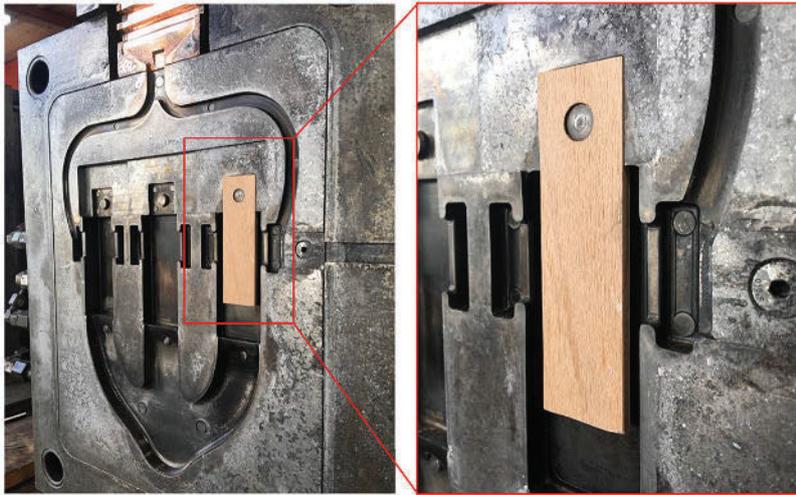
Fixiertes Holzeinlege­teil in der Druckgießform.
